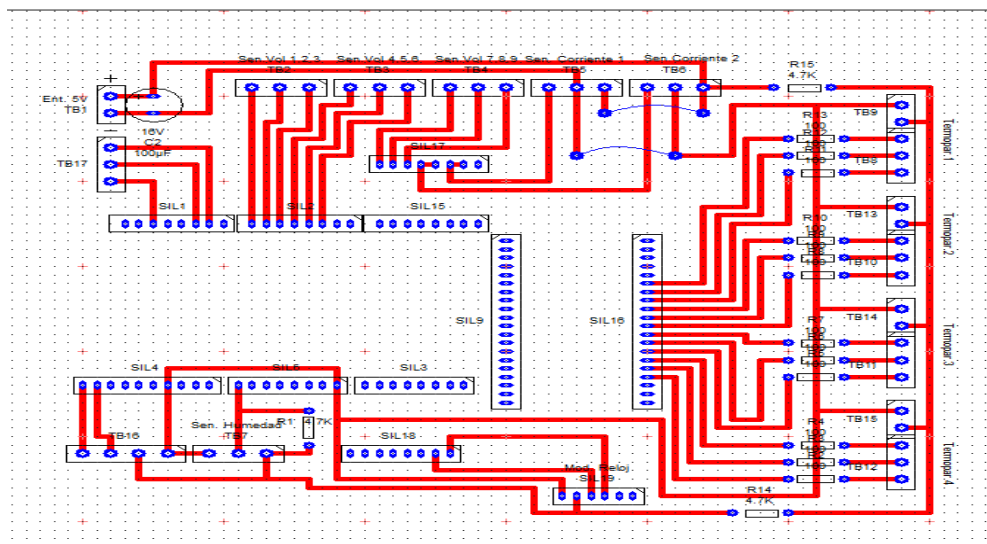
Diseño en PCB WIZARD Adquisición de Datos
